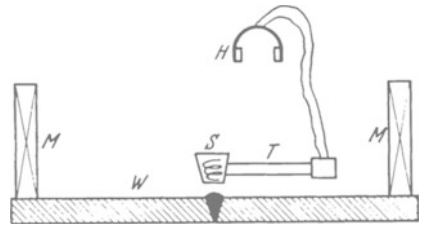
Grundform des IG-Schweißnahtprüfers.
